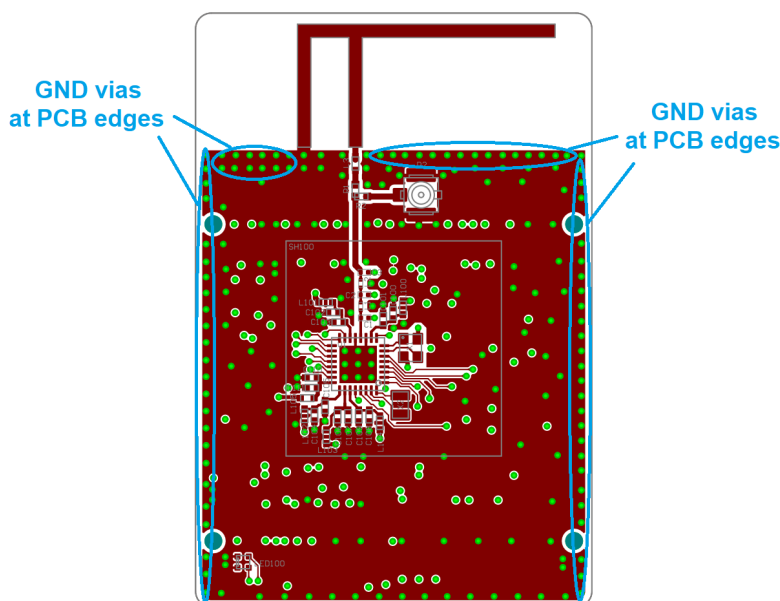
BRD4180A 射频板上 PCB 边缘的 GND 孔 (顶层)
